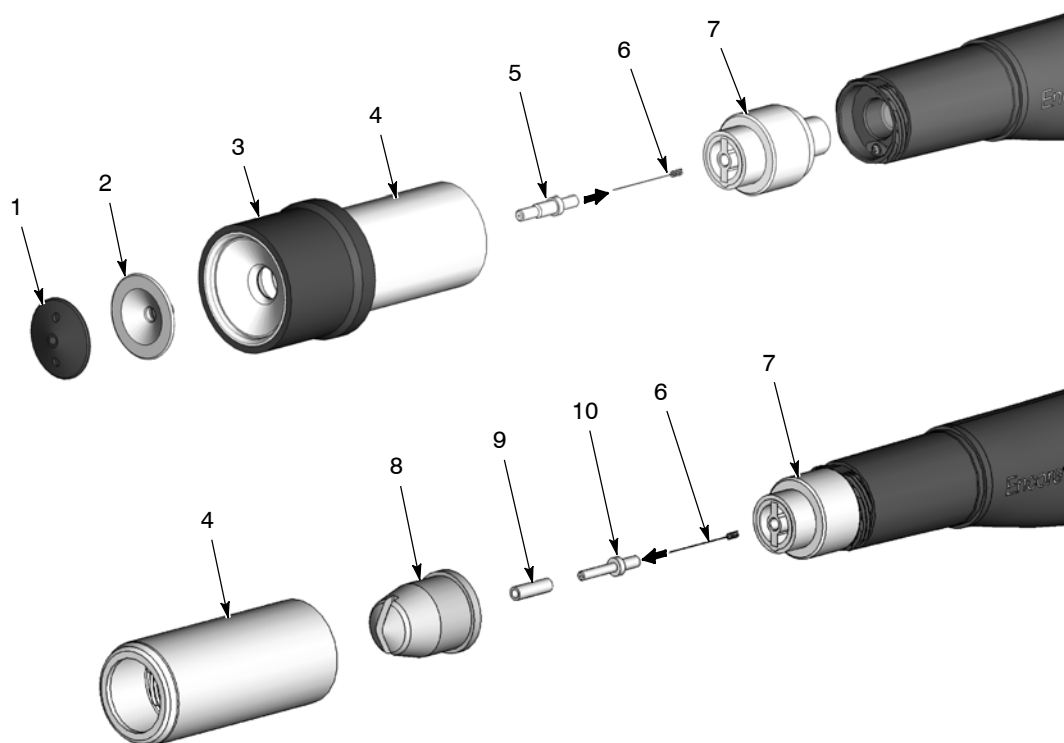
Schimbarea de la duza de pulverizare conică la plată sau de colț
